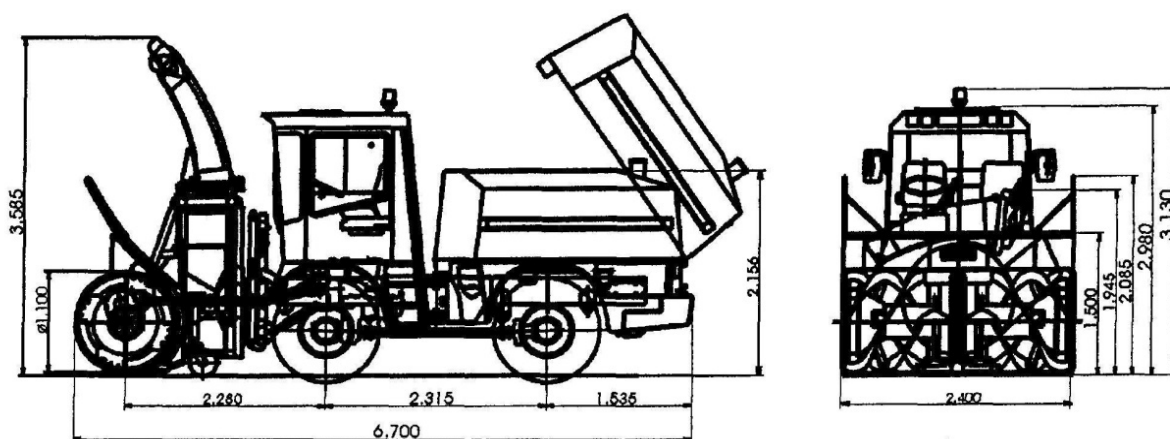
Габаритные размеры роторного снегоочистителя SCHMIDT SUPRA-5001
